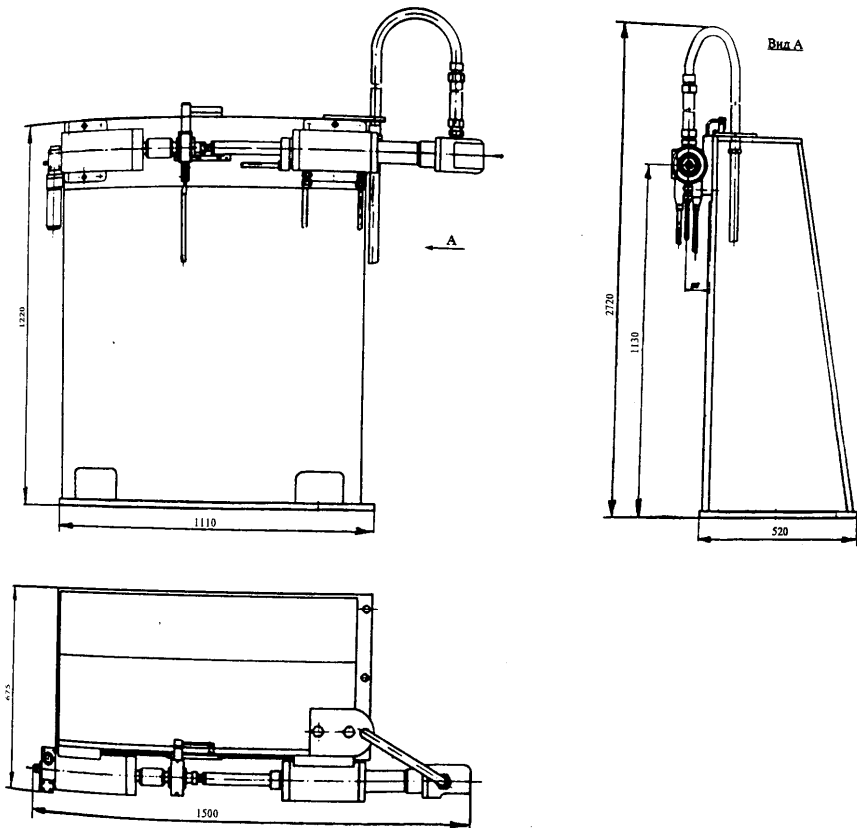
Верстат «Дуга-15» (загальний вид)
